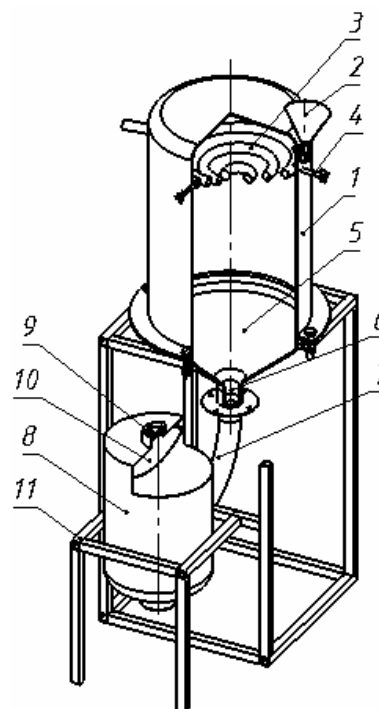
Пневматический смеситель со спиральной энергонесущей трубкой: 1 – камера; 2 – загрузочный патрубок; 3 – спиральная энергонесущая трубка; 4 – держатели; 5 – коническое днище; 6 – выгрузочный патрубок; 7 – труба; 8 – бункер; 9 – вентилятор; 10 – фильтр; 11 – рама
